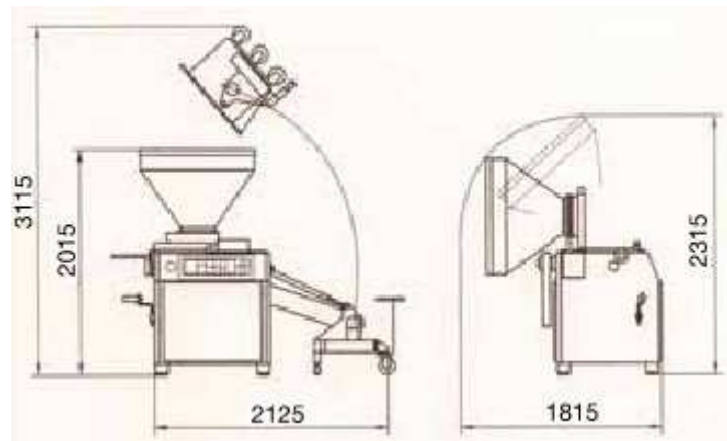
Detall constructiu d'un elevador de columna amb carro de 200 L en una embotidora (CastellVall, 2011)
